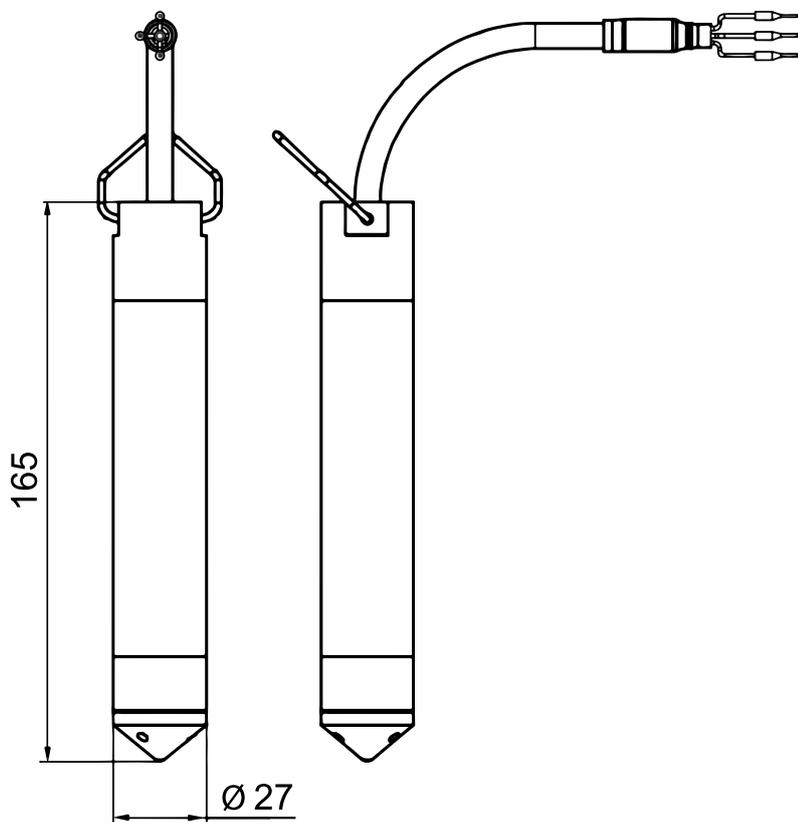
Габаритные и присоединительные размеры преобразователей ПД100-ДГ
